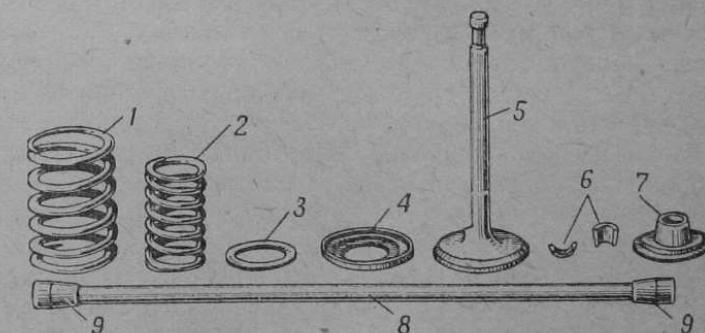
Детали верхнеклапанного механизма газораспределения двигателя М-76:
